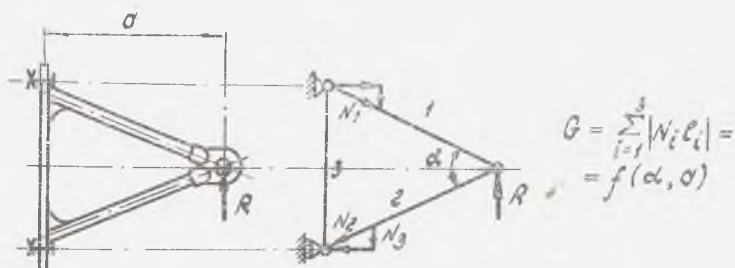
Словая схема и силовой вес кронштейна: 1, 2, 3 — номера стержней фермы
